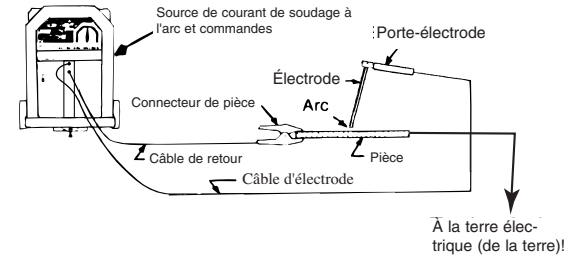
Circuit de soudage pour le procédé SMAW
